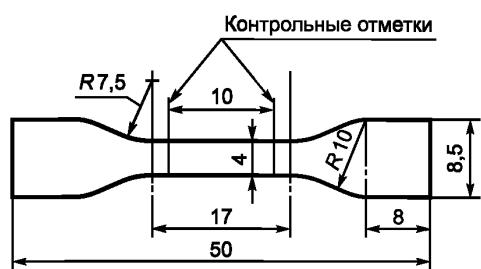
Образец в виде лопатки уменьшенного размера
